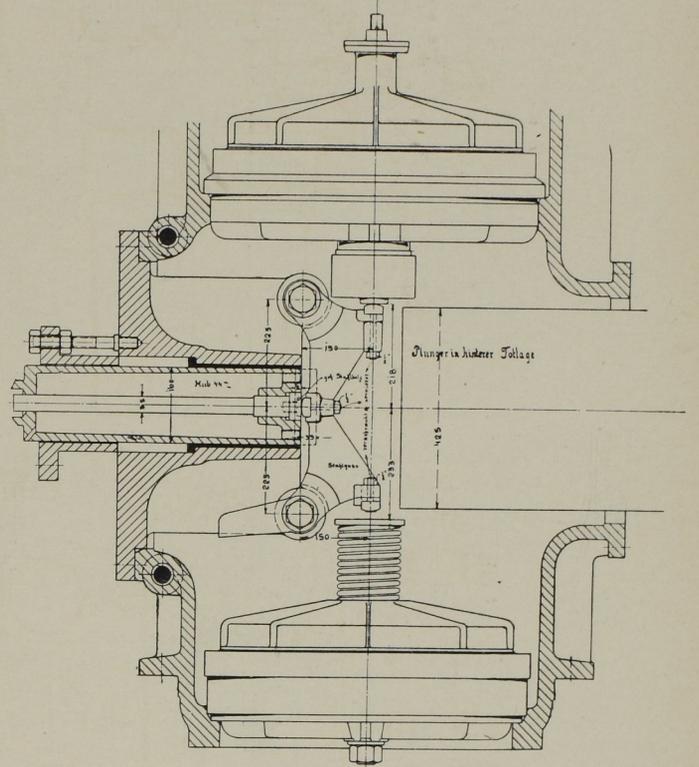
Pumpensteuerung mit Verdrängerkolben.
